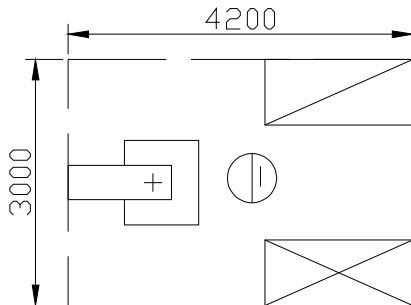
Схема организации рабочего места у сверлильного станка для высверливания и заделки сучков СВСА-2, F=12,6 м²
